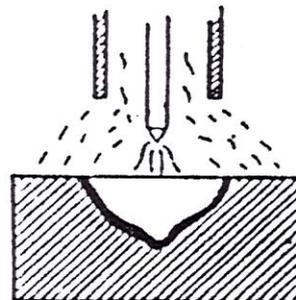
| Perfil de soldadura TIG con mezcla Ar - He.
